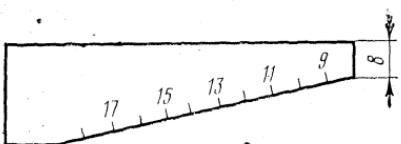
Шаблон для замера разрыва контактов контактора МКП-23
